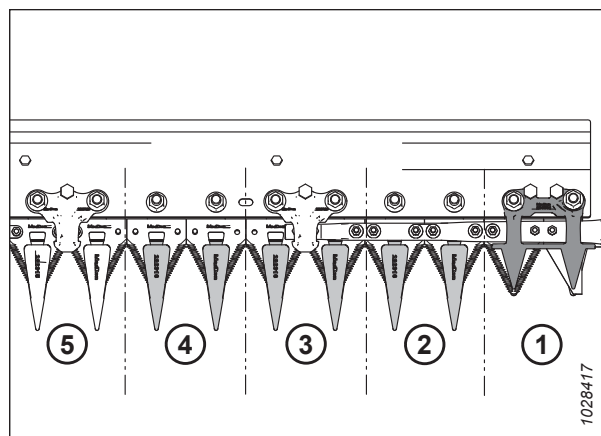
Doigt de couteaux pointus du côté de la conduite
